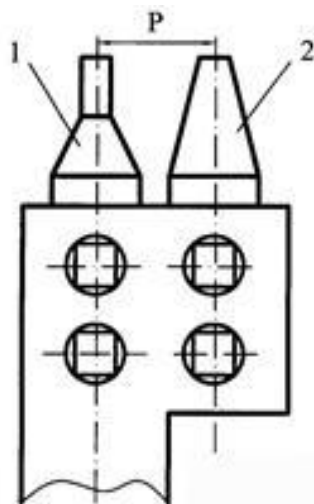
Резцовый блок для трапецевидальной резьбы
